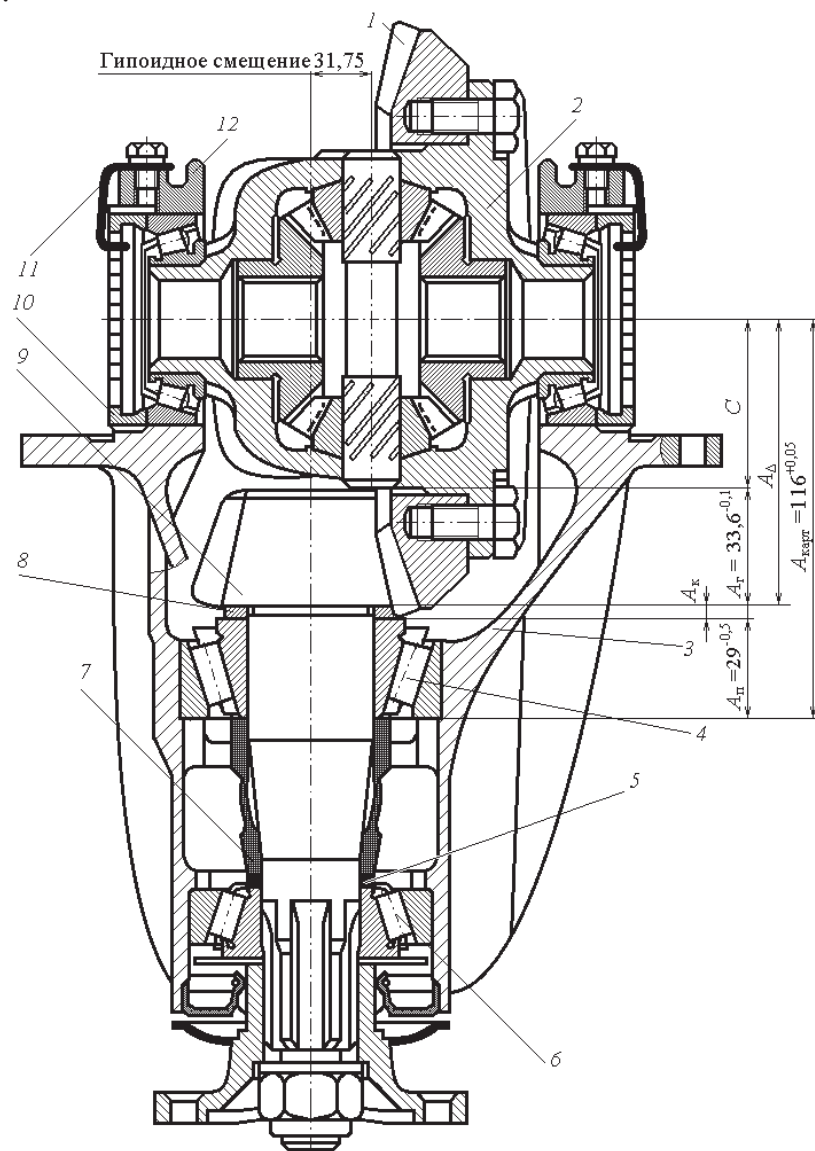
Схема редуктора заднего моста легкового автомобиля: 1 – ведомое колесо; 2 – коробка дифференциала; 3 – картер; 4 – задний конический роликовый подшипник; 5 – компенсатор (прокладка); 6 – передний конический роликовый подшипник; 7 – стальная распорная втулка; 8 – компенсатор (регулирующая прокладка); 9 – ведущее колесо; 10 – регулировочные гайки ведомого колеса; 11 – стопор регулировочной гайки; 12 – крышка подшипника дифференциала; A_k – толщина прокладки (компенсатора); A_Δ – монтажное расстояние ведущего колеса от оси ведомого колеса; C – контрольный монтажный размер колеса; A_r – высота головки колеса; $A_{карт}$ – размер проточки картера; A_Π – высота конического подшипника
